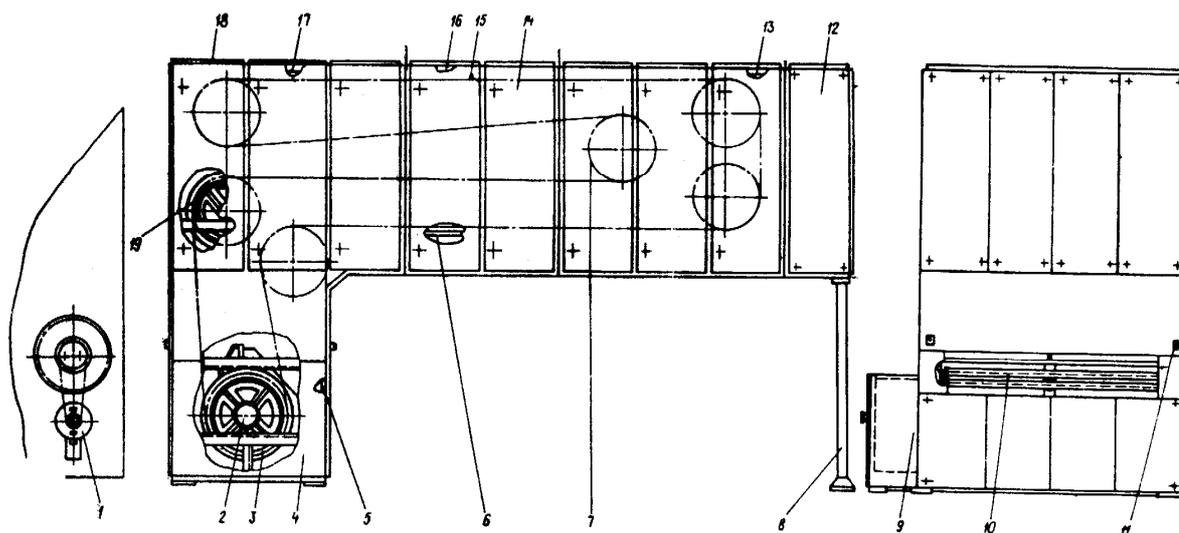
Общий вид универсального расстойного шкафа Т1-ХР2-Г:
